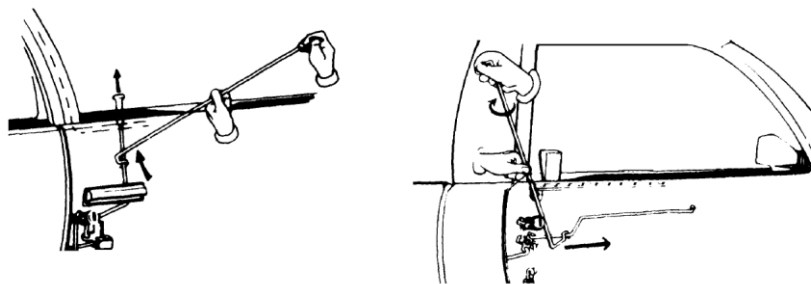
С помощью Z-образного приспособления можно быстро разблокировать тяги замков, расположенные как горизонтально (справа), так и вертикально (слева) (С разрешения компании Slide Lock Tool Company)
